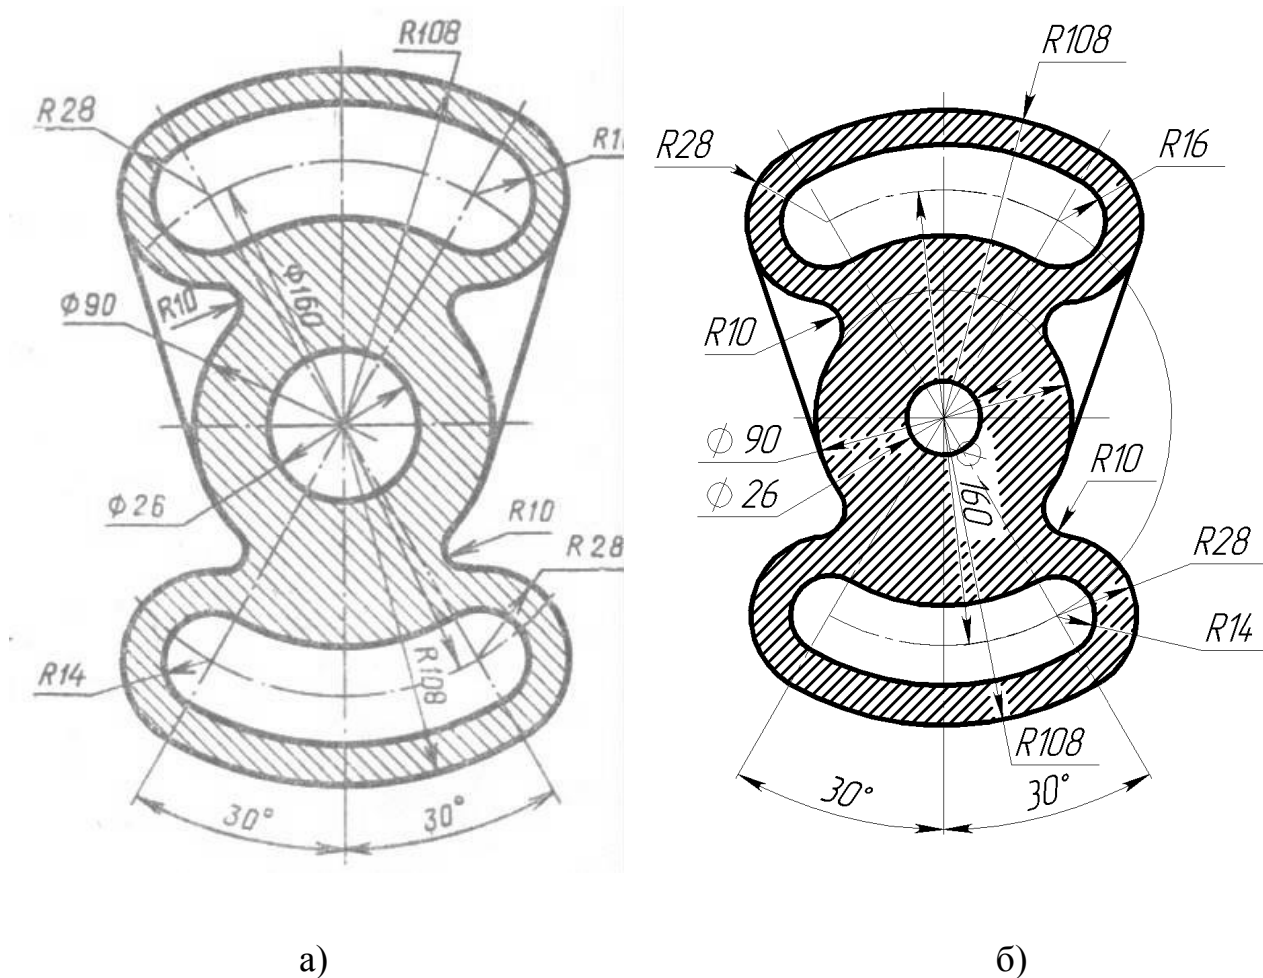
Остов: а) – задание; б) – готовый эскиз детали
